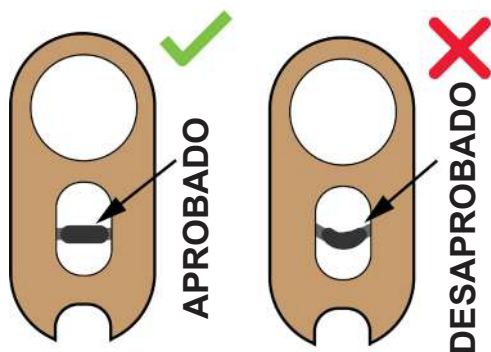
INSPECCIÓN DE COMPONENTES
